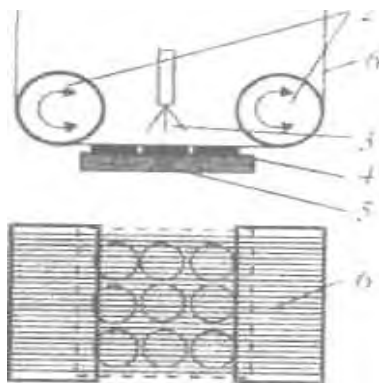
Схема станка проволочной резки: 1 - валики ведущие; 2 - валики ведомые; 3 - охлаждающая жидкость с абразивом; 4 - пластины или слитки полупроводникового материала; 5 - стол; 6 - проволока
